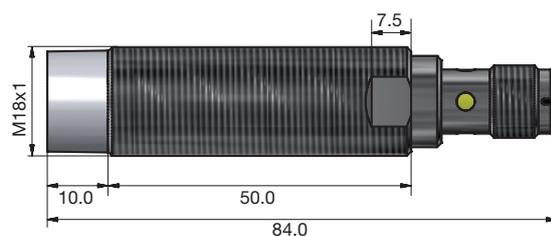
Lange Ausführung, bündiger Einbau, Kabel
